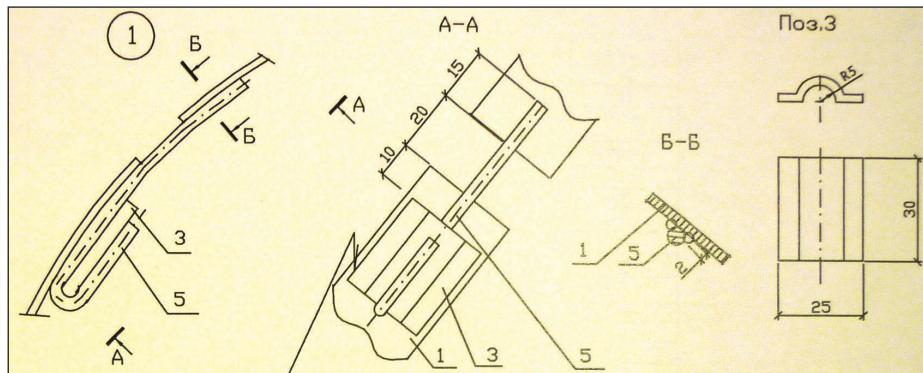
Скоба и штырь для закрепления опорного кольца на конструкции
